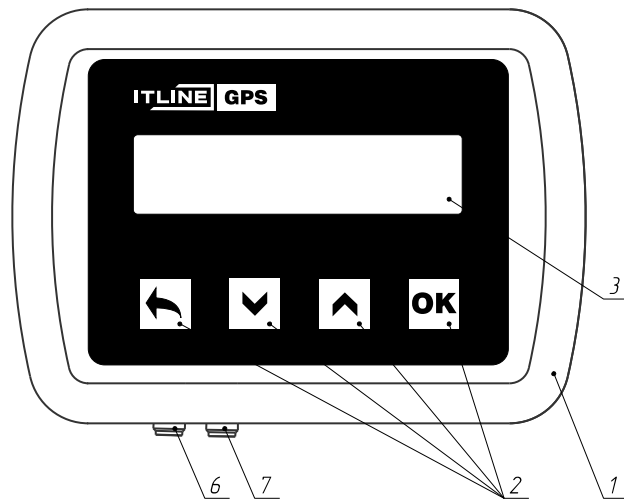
Внешний вид изделия сверху. Компактное базовое исполнение.
